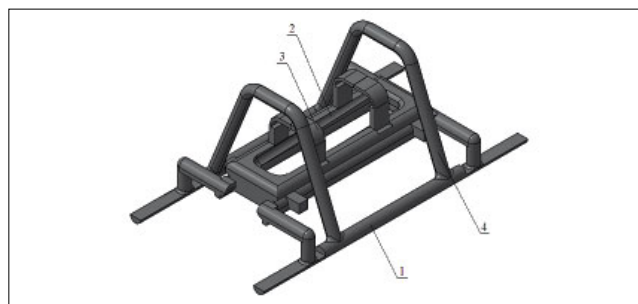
Крепление резервуара с БПЛА: 1 – опорные стойки; 2 – форма под емкость; 3 – раздвижные фиксаторы емкости; 4 – ножки для БПЛА
